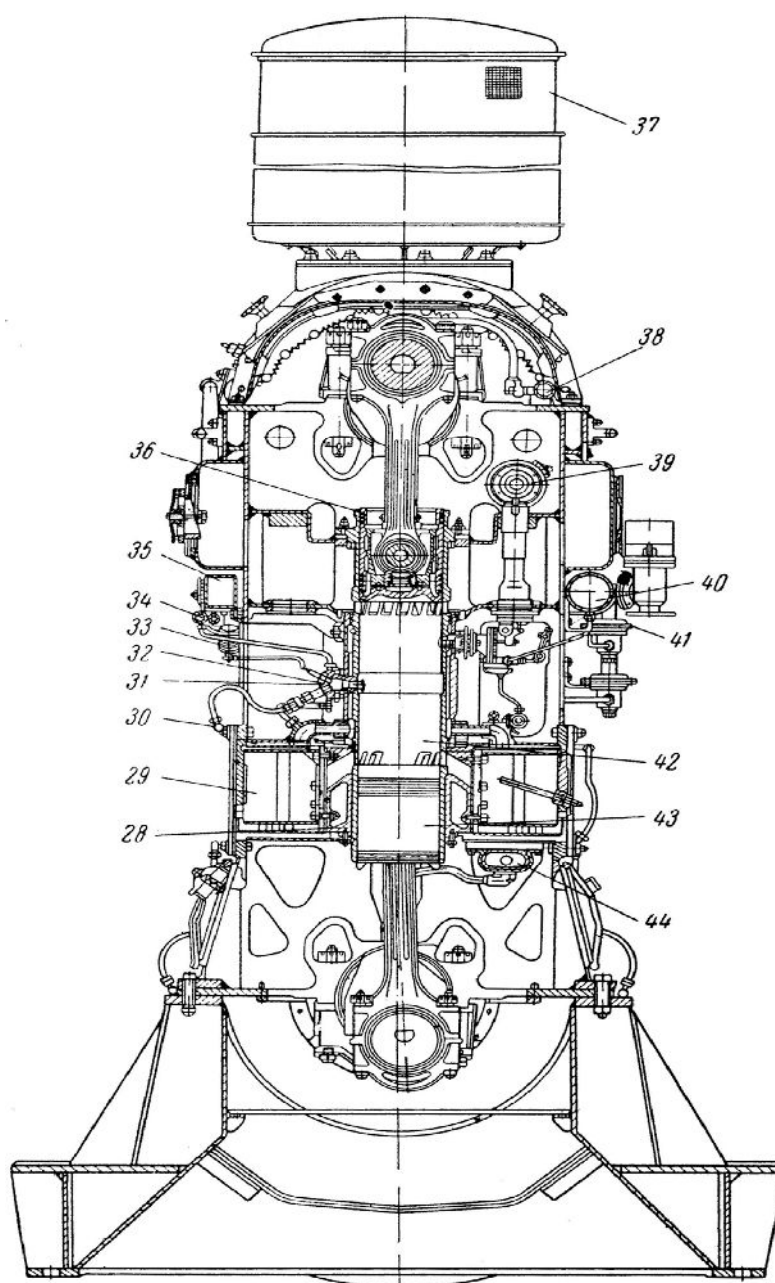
а Газовый двигатель 11ГД100. Поперечный разрез [6]
